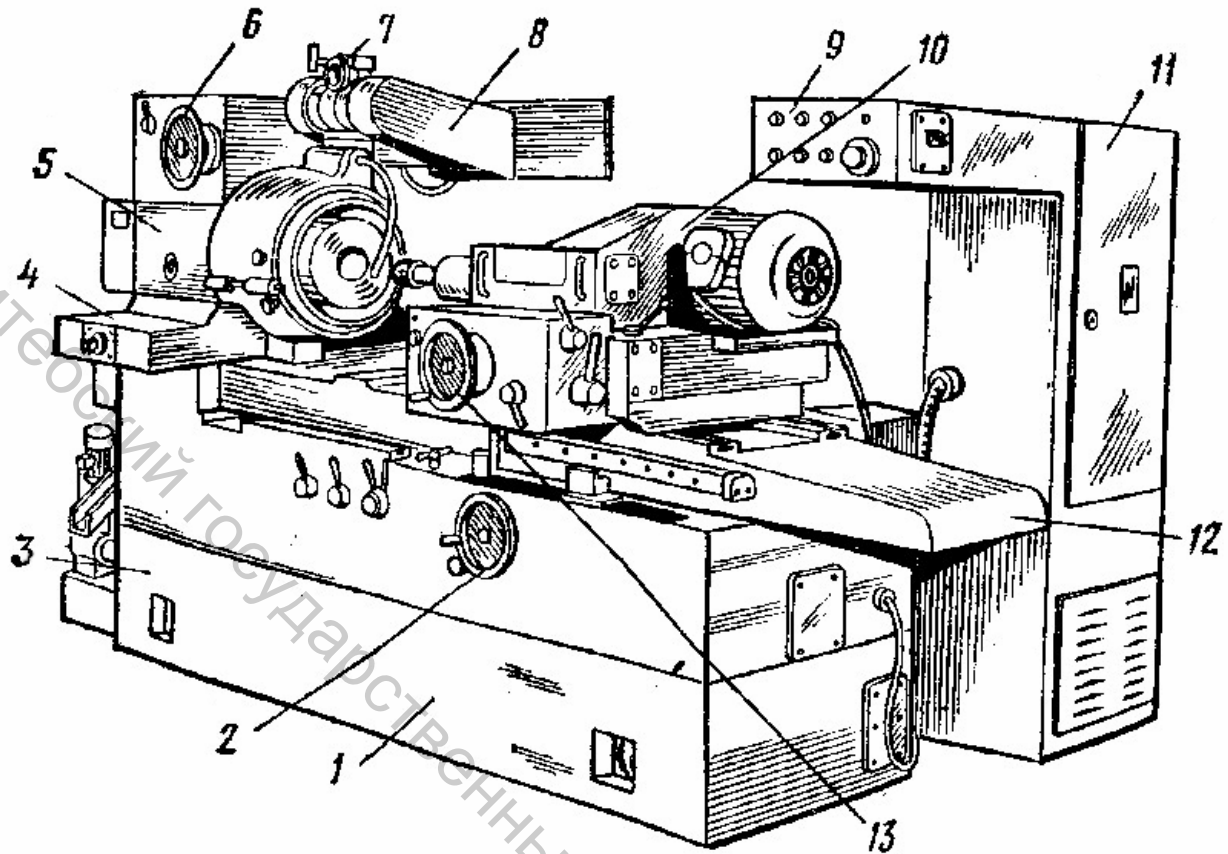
Универсальный внутришлифовальный станок 3К228В.
